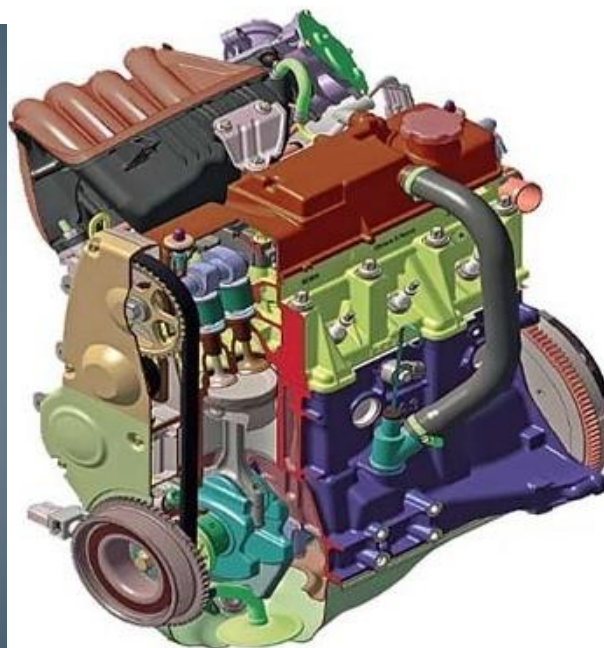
Общий вид двигателя ВАЗ-11186, взятого как базовый для расчета
